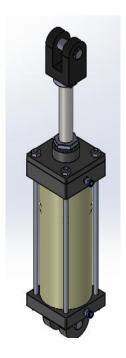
Diseño CAD de un cilindro neumático con pistón. (Fuente: Autor).
